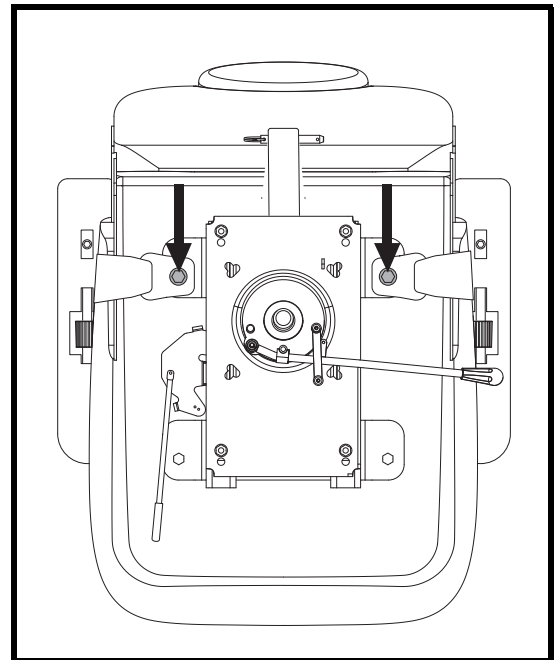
Befestigungsschrauben des Rückhaltegurtes
